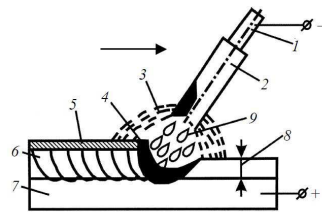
Схема ручного дугового зварювання металевим електродом з покриттям: 1 – металевий стрижень; 2 – покриття електроду; 3 – газова атмосфера дуги; 4 – зварювальна ванна; 5 – затверділий шлак; 6 – метал шва; 7 – основний метал; 8 – глибина проплавлення; 9 – краплі розплавленого електродного металу
